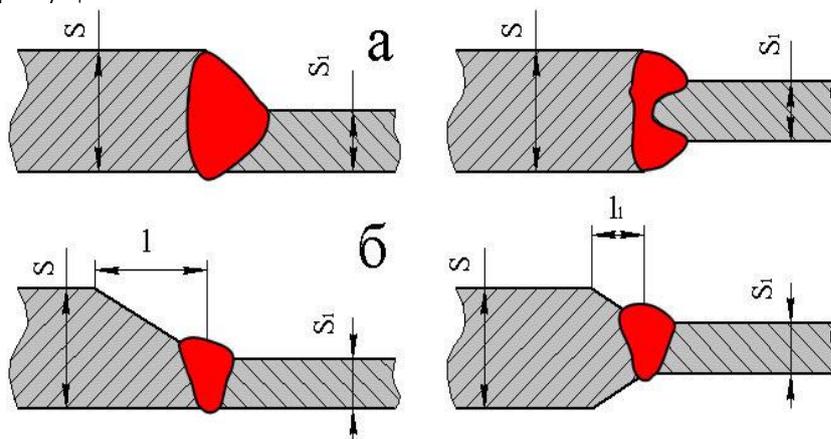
Сварка исходных заготовок различной толщины:
